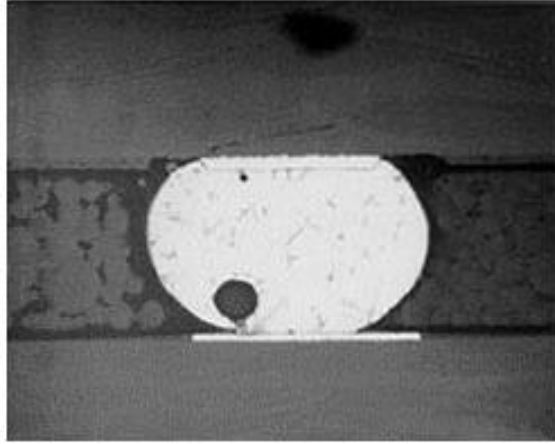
Sección transversal de una unión de soldadura BGA que muestra la presencia de un vacío [2].
